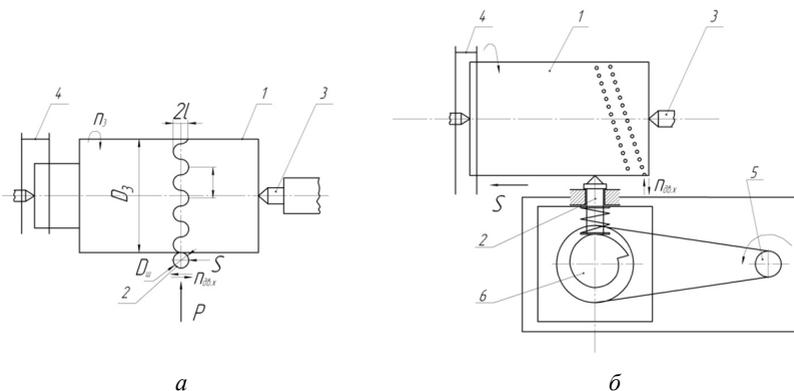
Схемы формирования регулярного микрорельефа на цилиндрической поверхности вибрационным пластическим деформированием: *a* – виброобкатыванием; *б* – чеканкой;
